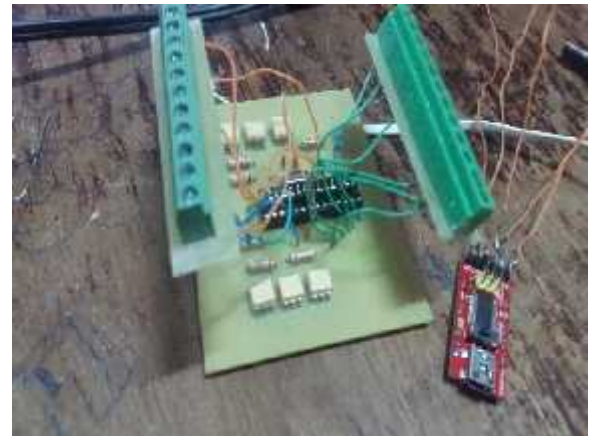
Componentes Soldados en la tarjeta
